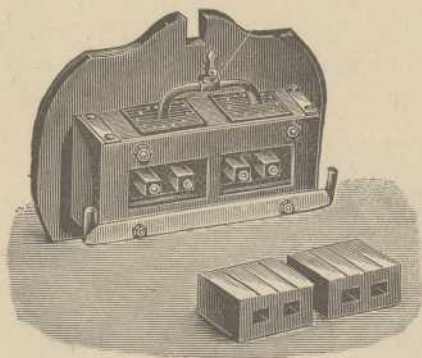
Boquilla de una prensa de ladrillos perforados.
